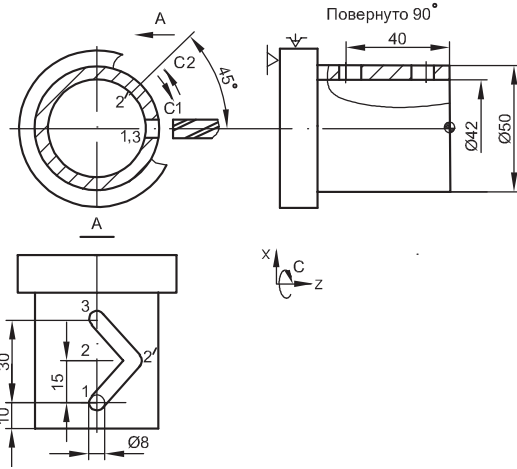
Циліндрична інтерполяція. Фрезерування ламаного паза
